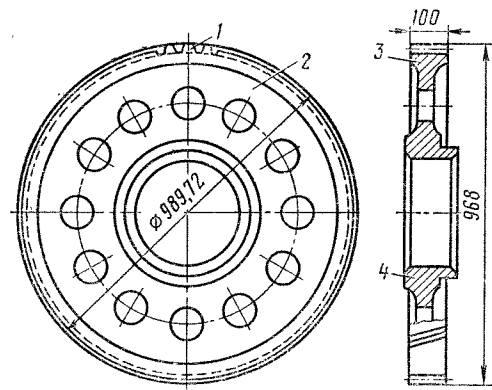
Зубчатое колесо тяговой передачи электровоза ВЛ10
